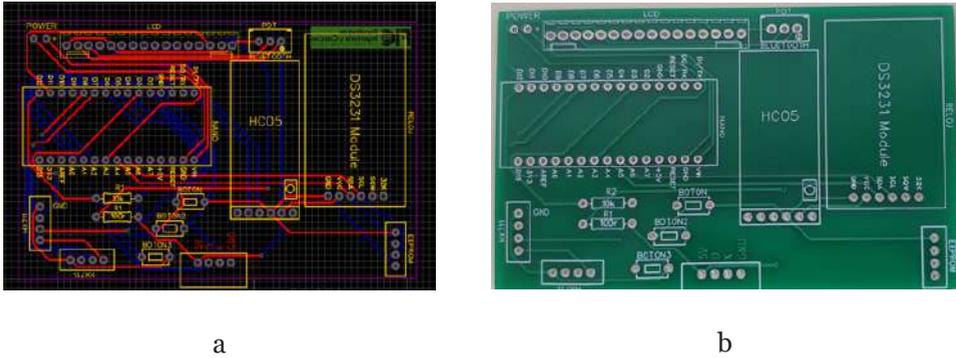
(a) Diseño del PCB generado, (b) Diseño del PCB impreso.
